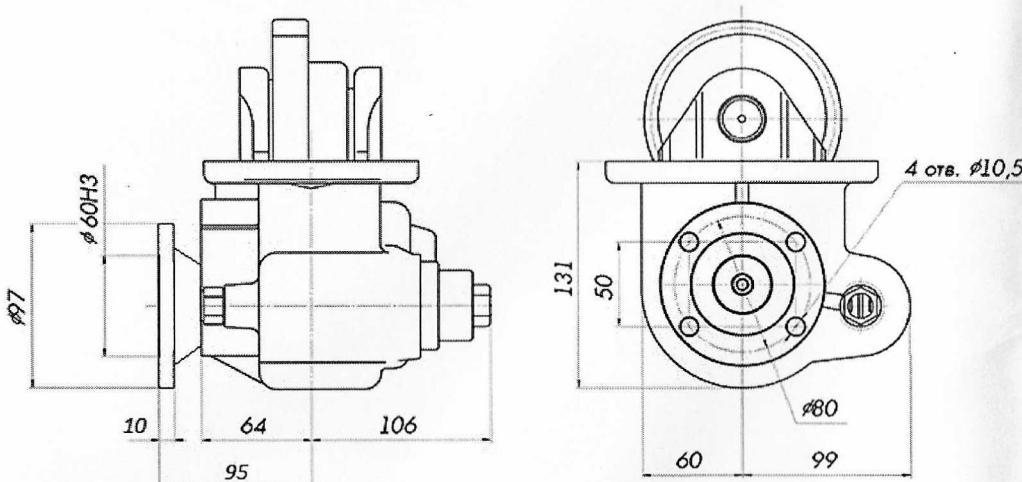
Габаритные и присоединительные размеры HDX M03P1 FLC 03
